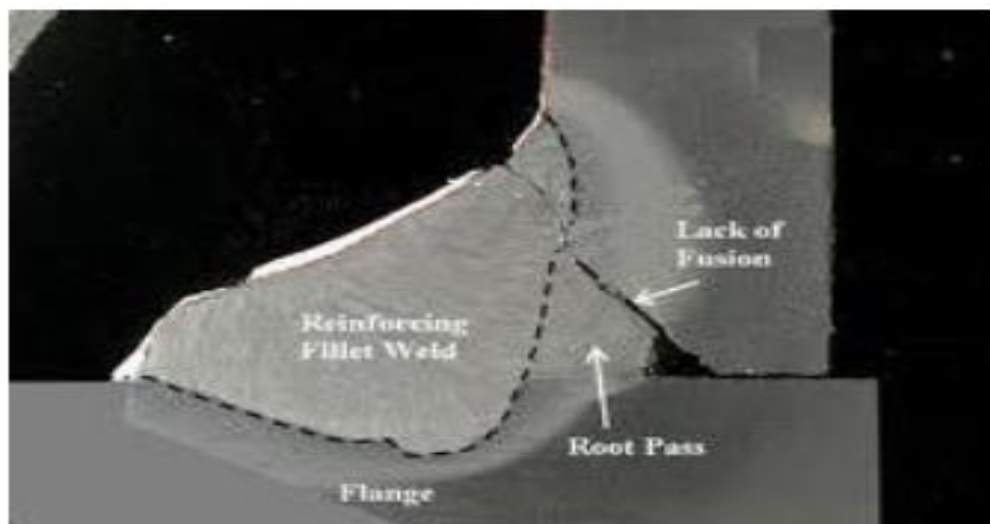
Manque de fusion à la racine de la soudure :
